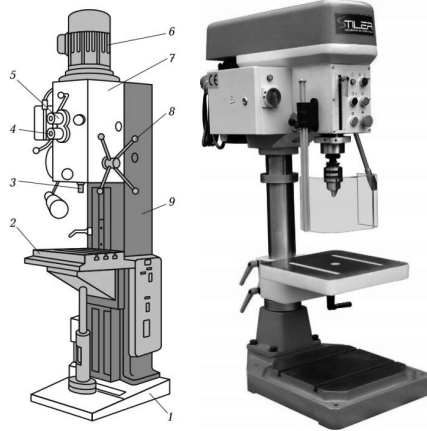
Вертикально-свердильний верстат: 1 – фундаментна плита; 2 – стіл; 3 – шпиндель; 4 – коробка подач; 5 – коробка швидкостей; 6 – електричний двигун; 7 – свердильна головка; 8 – рукоятка; 9 – колона
